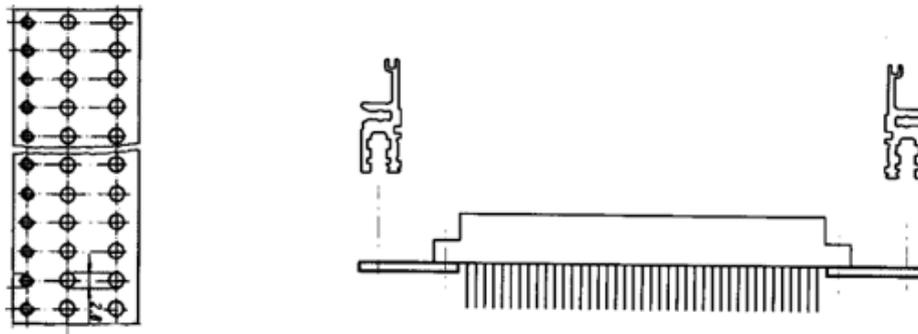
Примеры конструкций опорной планки (а) и кодировочного блока для субблока eurocard PRO (б) немецкой компании Schroff
